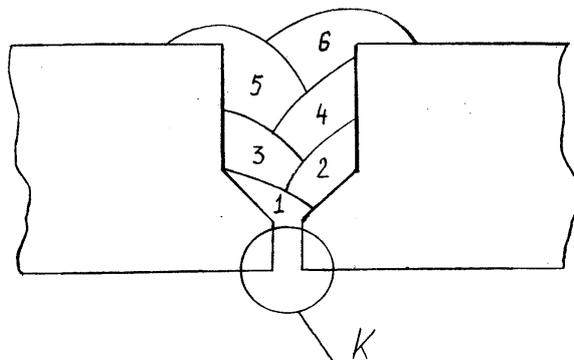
Рекомендуемая схема положения сварных слоев параллельными проходами (для кольцевых стыков трубопроводов):
